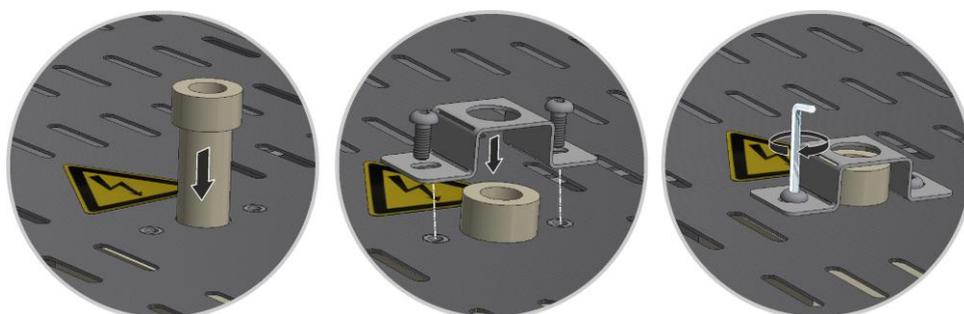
Montagem do tubo do ar de exaustão (semelhante à figura)
